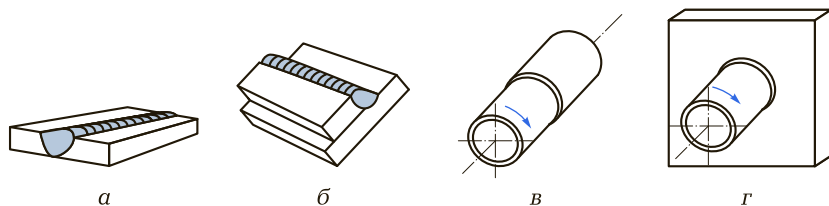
Положение при сварке стыковых и тавровых швов:
